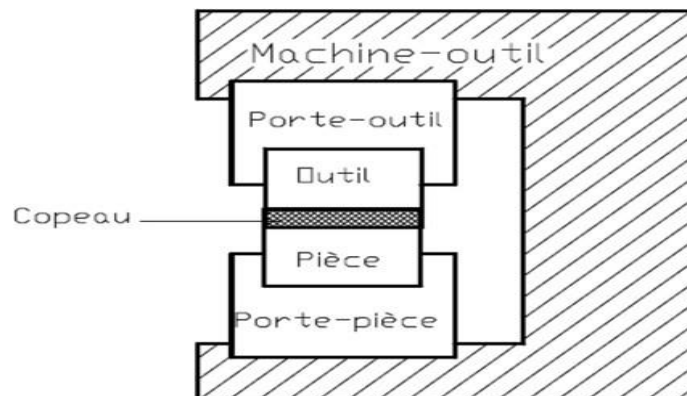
Schéma de procédés d'usinage d'une pièce. [2]
